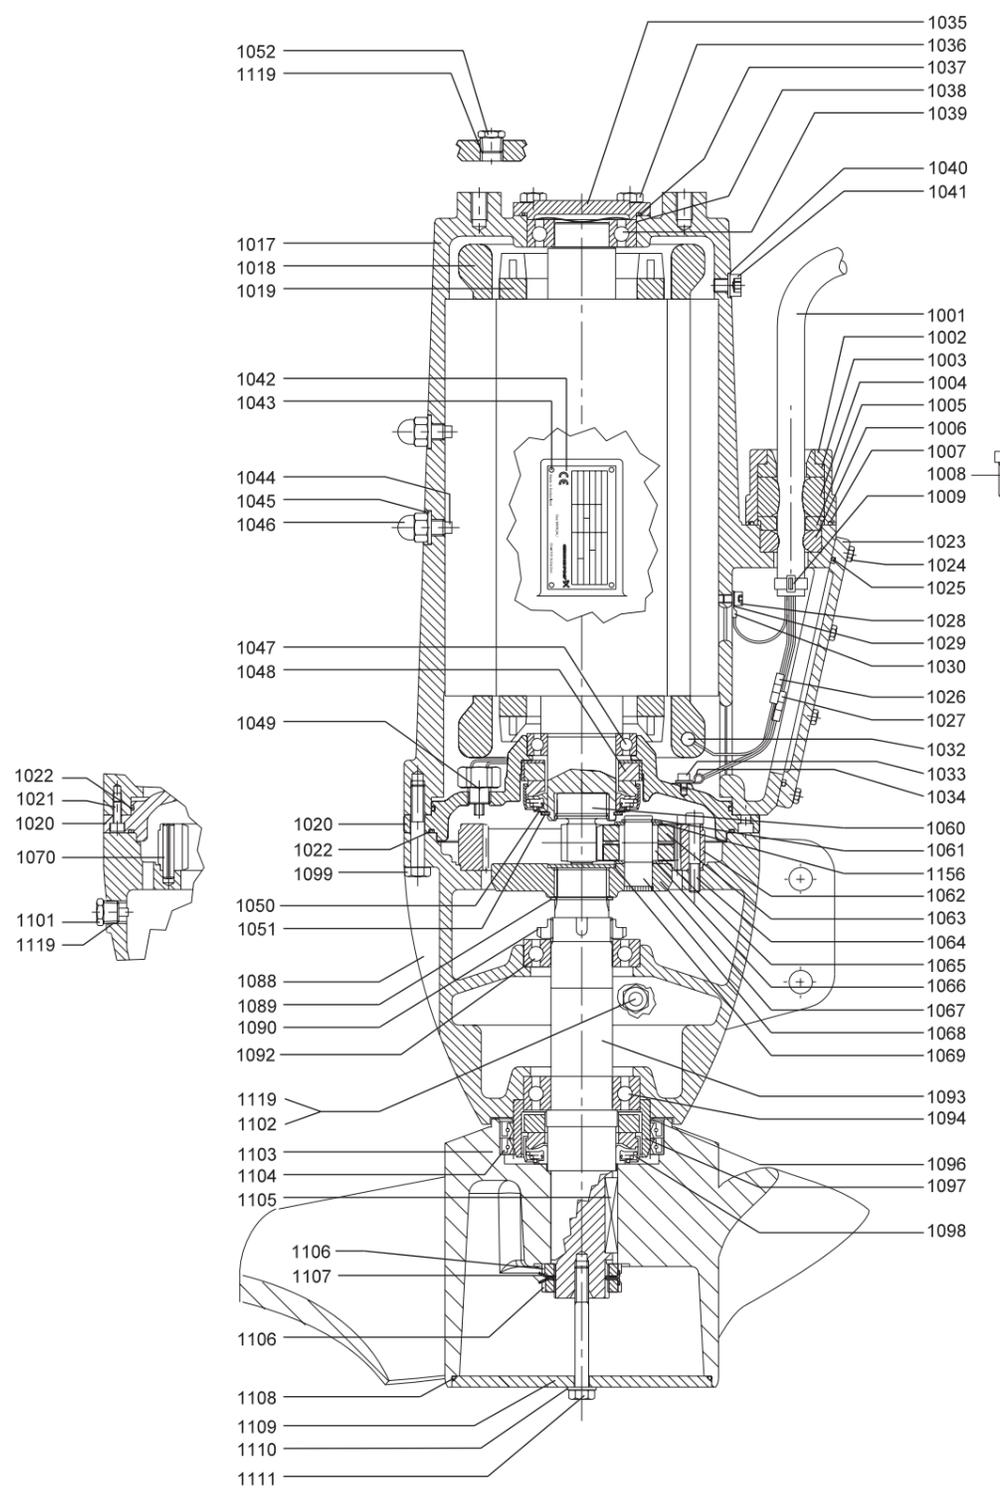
Чертёж в разрезе, SRP.xx.30.xx
